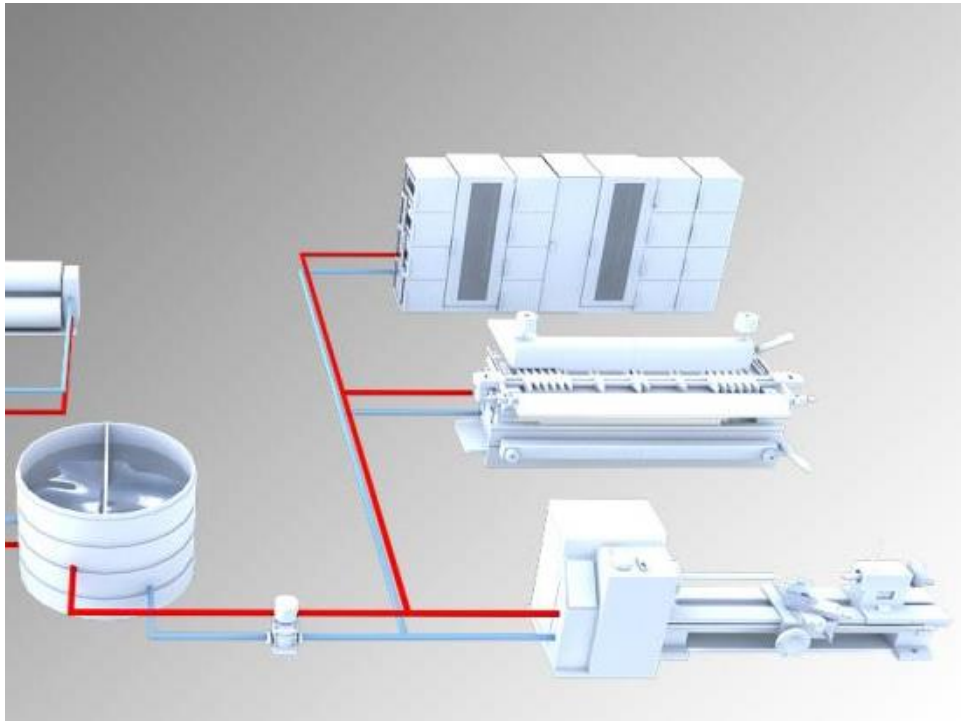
Kompaktní chiller [10]
